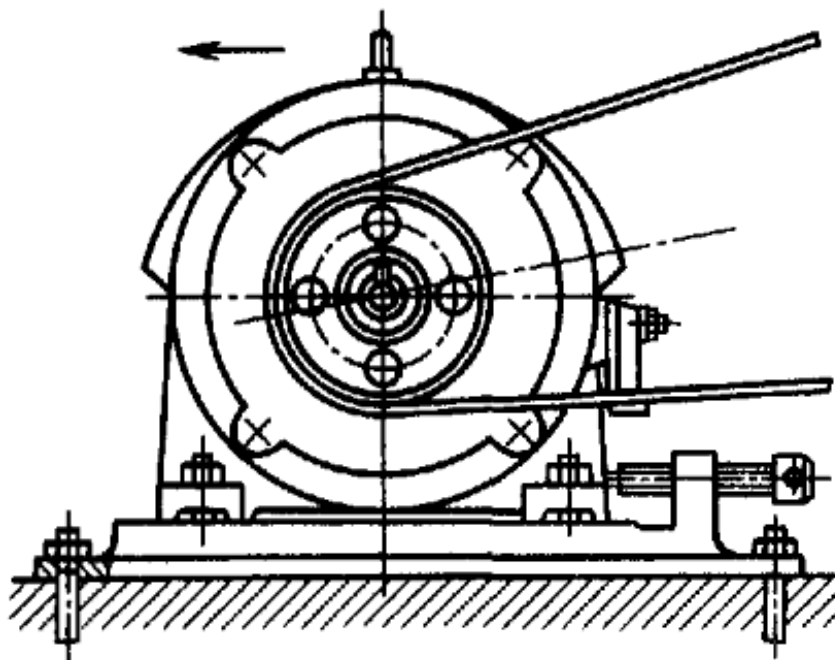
Устройство для натяжения ремней перемещением одного из шкивов
